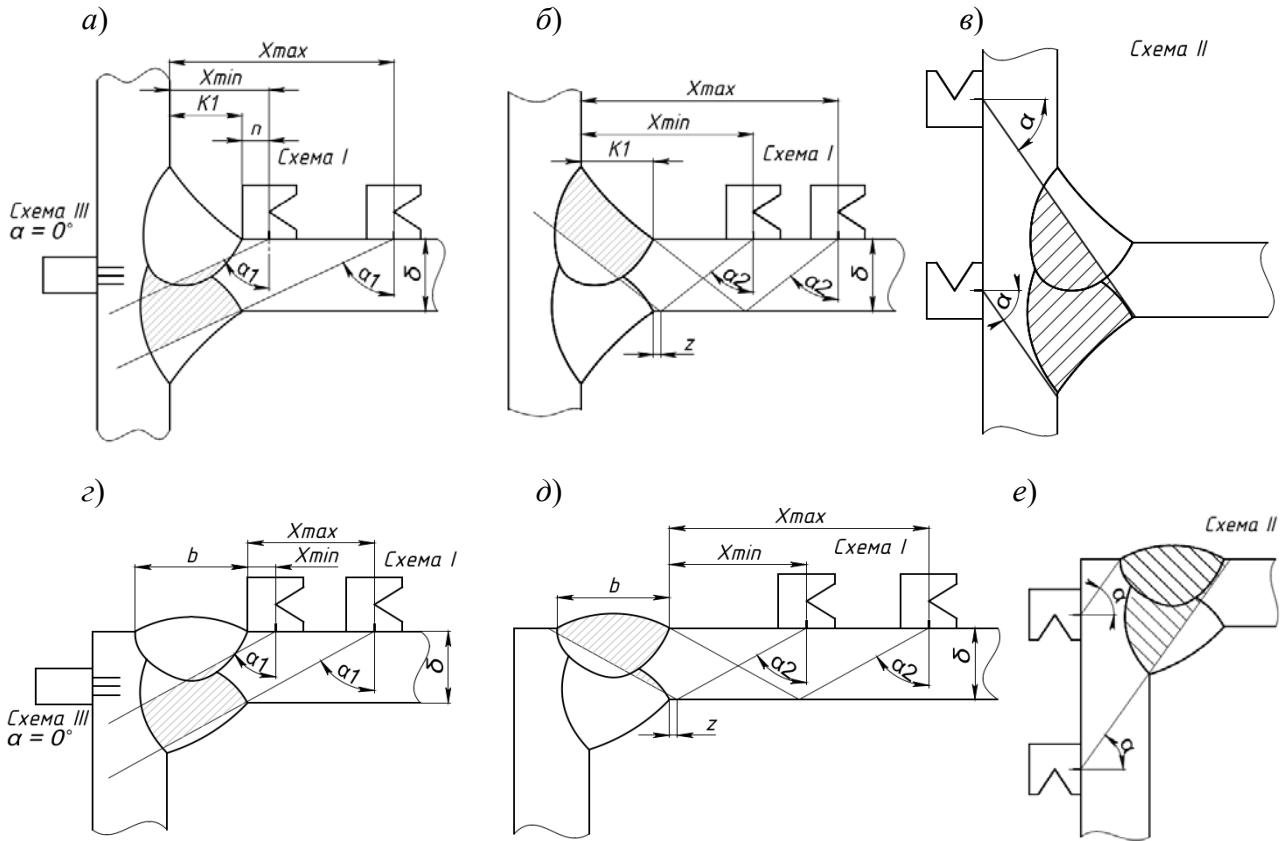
Схемы контроля тавровых (а, б, в) и угловых (з, д, е) сварных соединений
